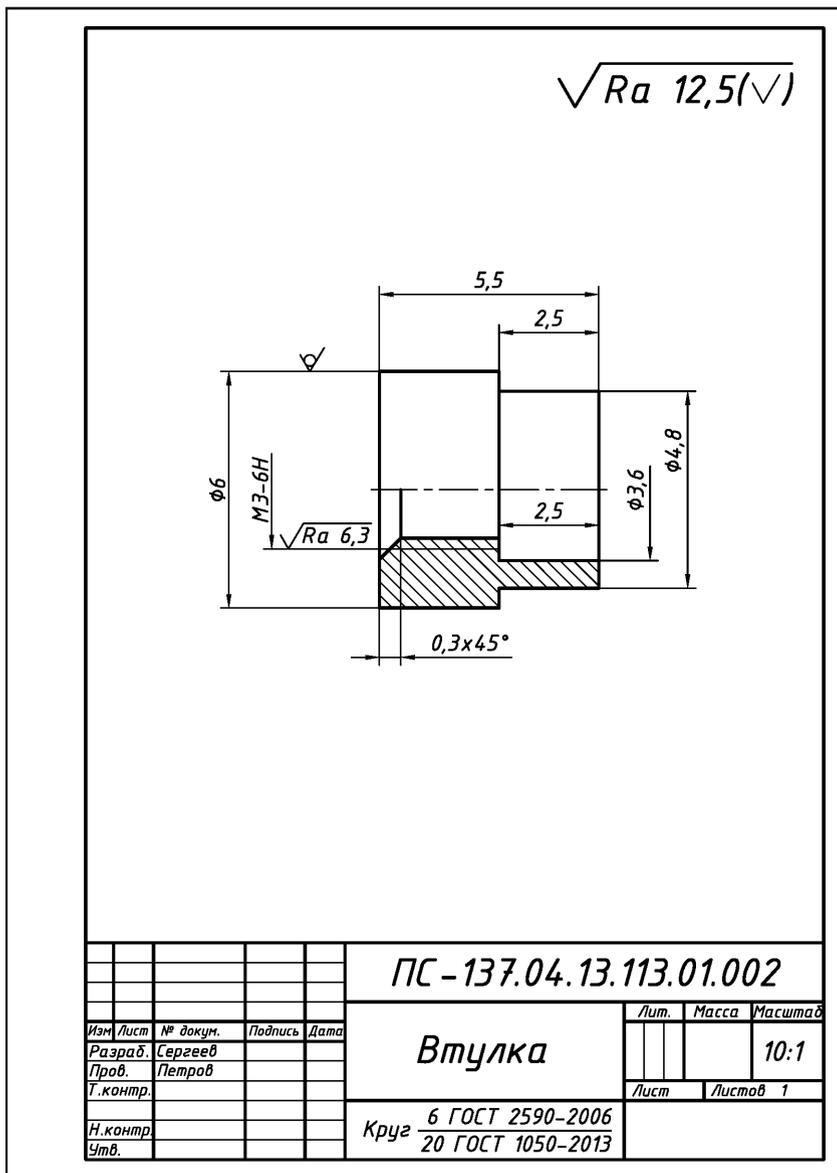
Оформление рабочего чертежа детали «Втулка»
